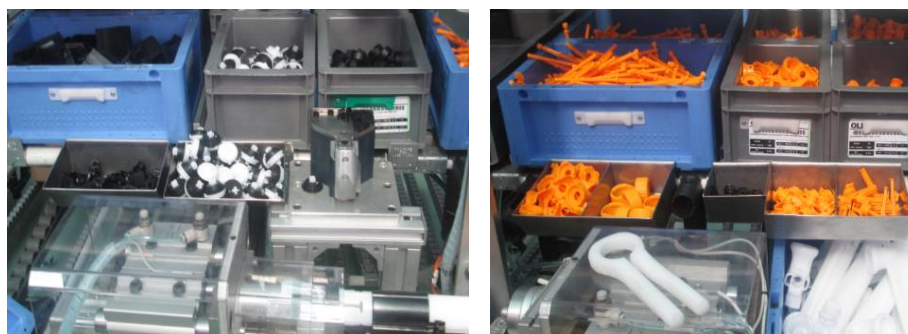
GAVETAS E DISPOSITIVOS DE MONTAGEM TB005
